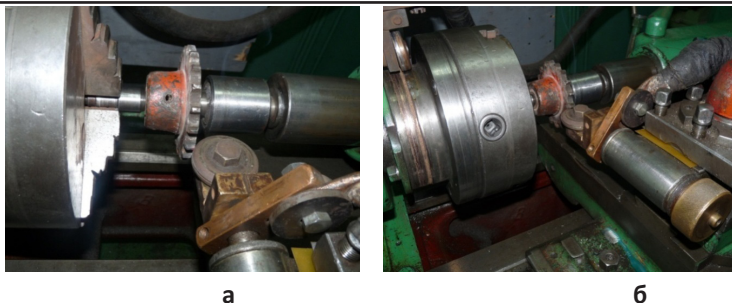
Варианты ЭМЗ звездочек цепной передачи: а – ЭМЗ боковых поверхностей зубьев звездочки при $I = 600$ А, $v = 100$ мм/мин, $P=30$ Н; б – ЭМЗ зубьев звездочки по впадине при $I = 3000$ А, $\tau = 3$ с, $P=30$ Н
